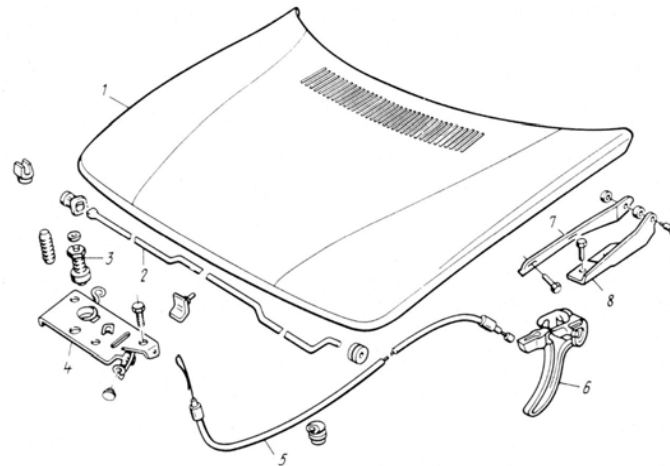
Капот двигателя автомобиля с механизмом открывания:
